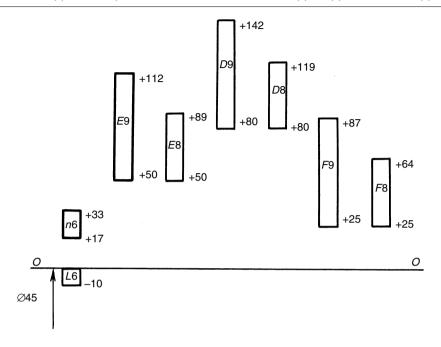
Схемы расположения полей допусков посадок крышки в корпус:
